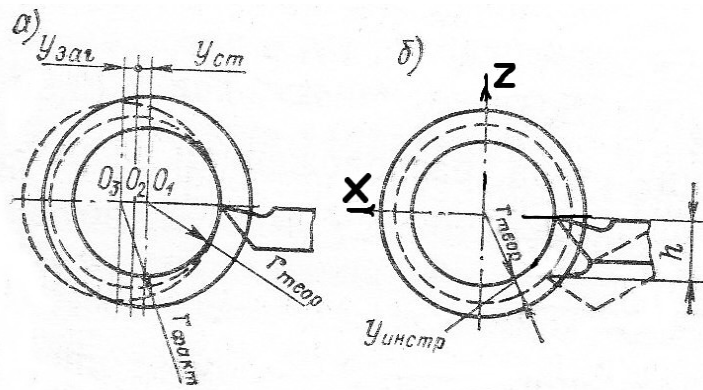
Влияние упругих отжати на размер обрабатываемой заготовки
